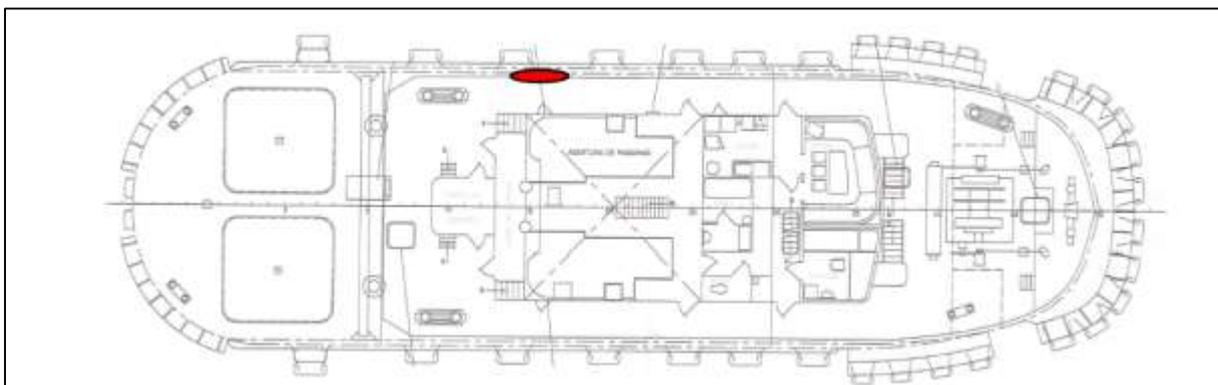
Se muestra posición aproximada del daño producido en banda de babor en la vista en planta del B/R Rúa II. Fuente: Plano arreglo general
